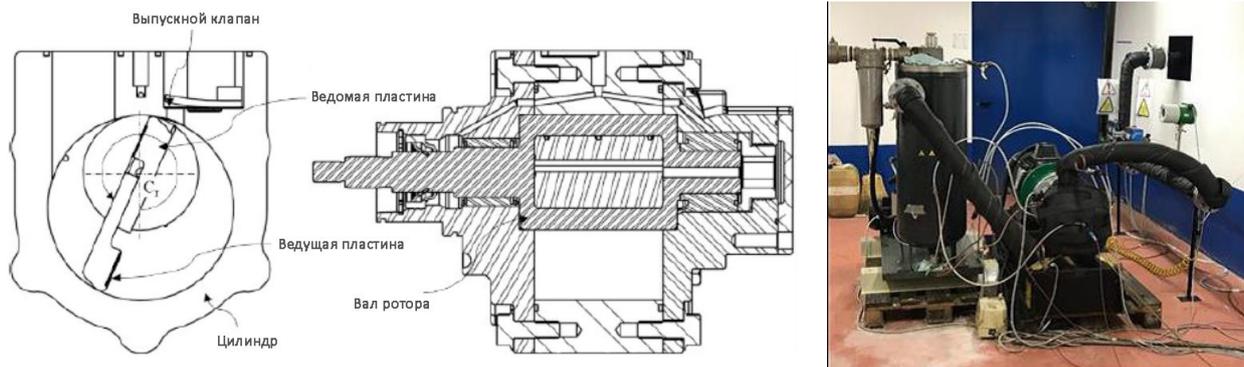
Схема двухлопастного компрессора и экспериментальный паровой расширитель
